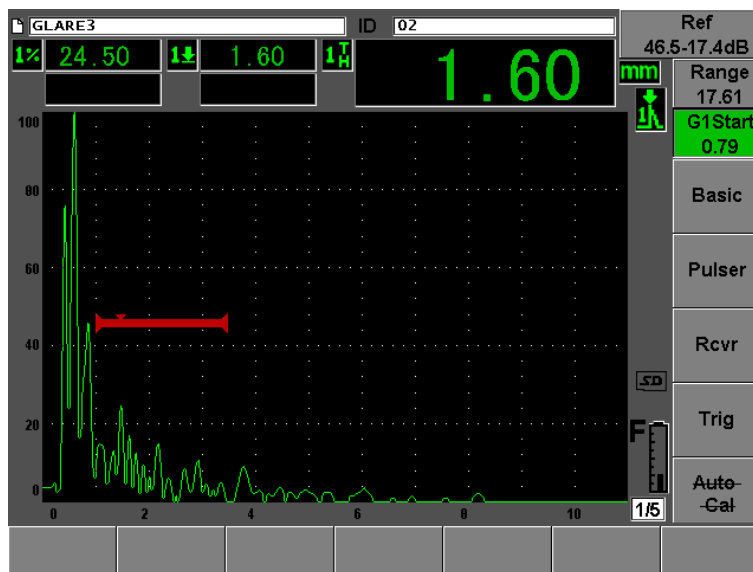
Defeito encontrado a 0.95 mm da superfície do GLARE.
